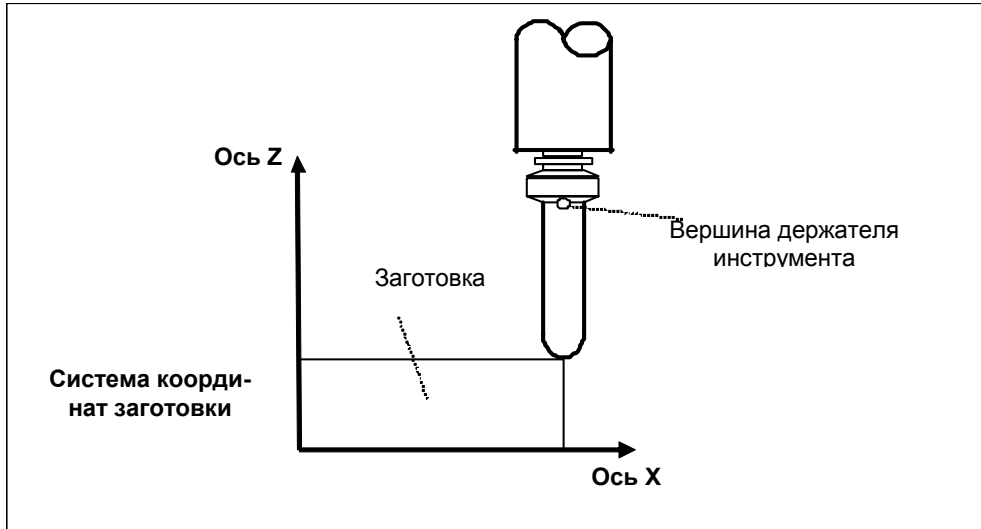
(i) Если отсутствует погрешность установки заготовки
